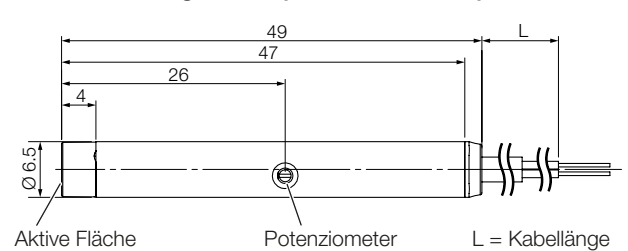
Aufbau der Ausführungen mit 6,5-mm-Gehäuse
